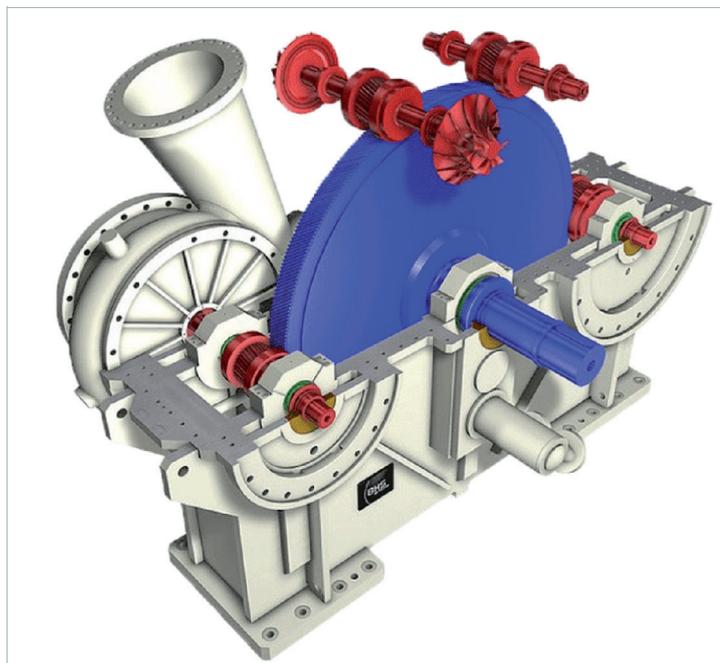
Explosionszeichnung eines mehrstufigen Zentrifugalverdichters.
